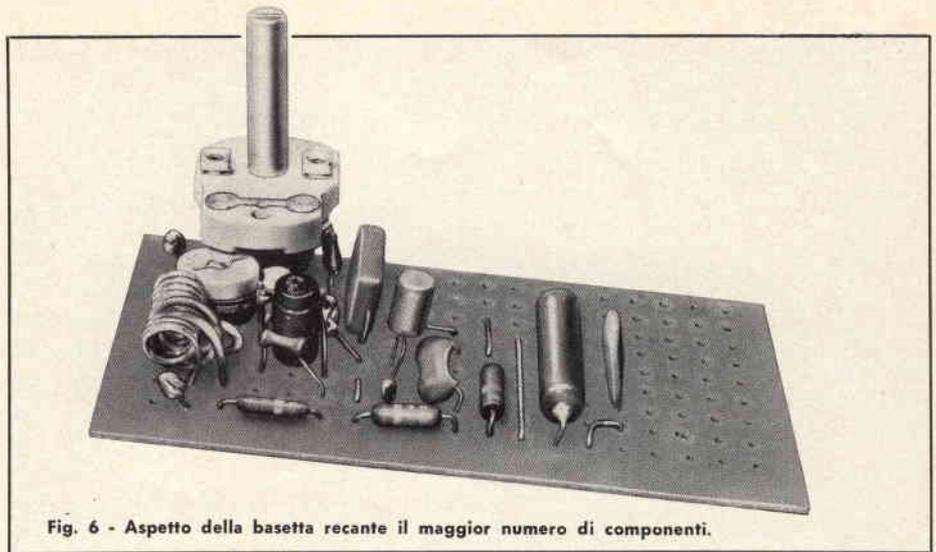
Aspetto della basetta recante il maggior numero di componenti.
